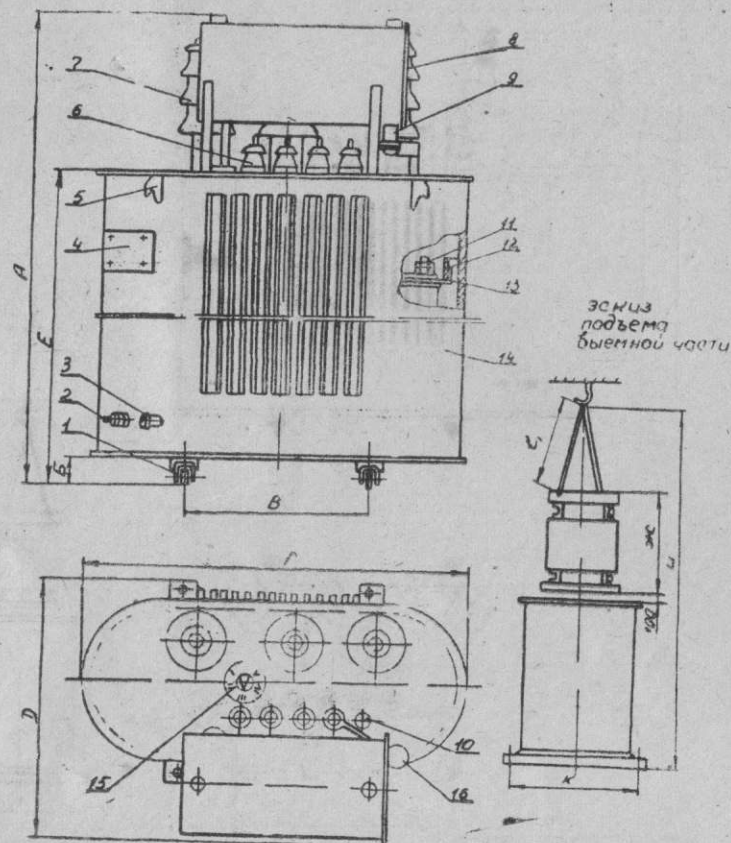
1-ролик трансформаторный; 2-заземление; 3-пробка для заливки и отбора пробы масла; 4-щиток мощности; 5-крюк для подъема трансформатора; 6-ввод НН; 7-ввод ВН; 8-маслоуказатель; 9-воздухоосушитель; 10-ртутный термометр; 11-гайка; 12-скоба; 13-пластина; 14-бак; 15-переключатель; 16-предохранитель (устанавливается по требованию заказчика).
